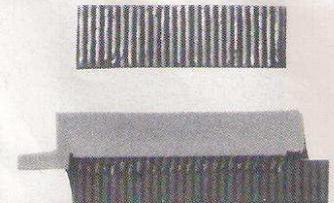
Connecteur 60 pistes soudé à l'arrière du connecteur Card Edge
